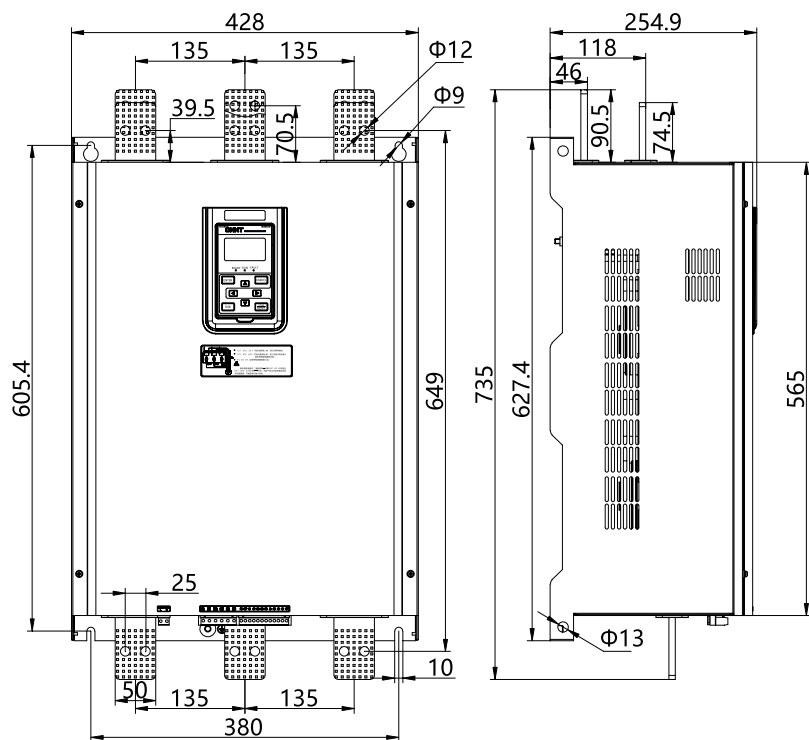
Общий компоновочный и установочный габаритный чертеж для устройств моделей NJRP5-710/D4–NJRP5-1000/D4 и NJRP5-710/D6–NJRP5-1000/D6
